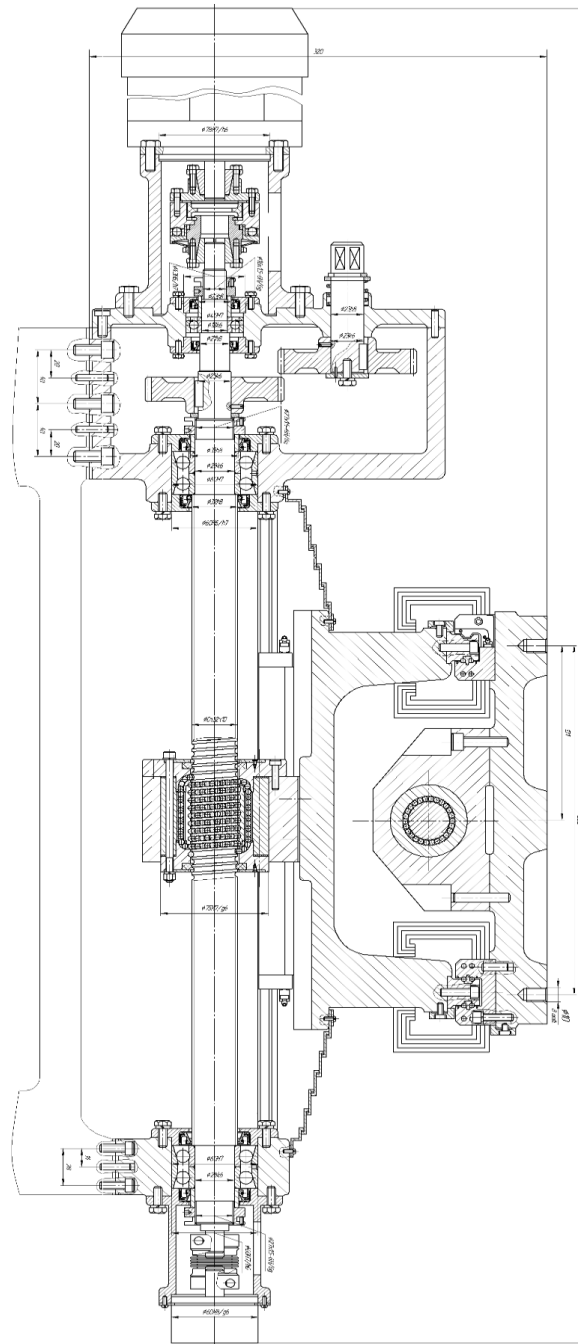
Горизонтальний привід поздовжньої подачі хрестового багатоцільового столу свердлильно-фрезерно-розточувального верстата з ЧПК:
